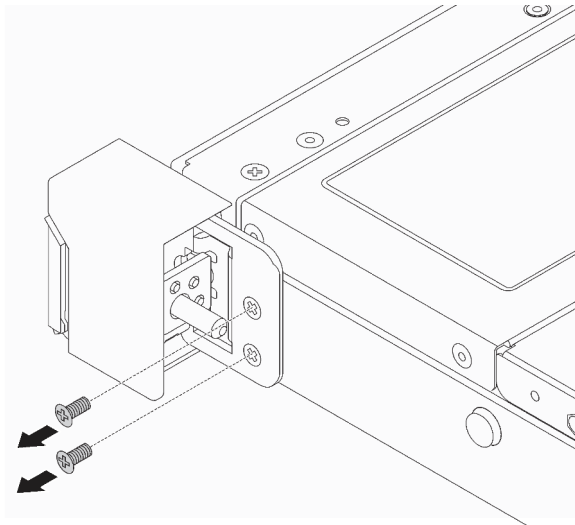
Entfernen der Schrauben der Rack-Verriegelung
